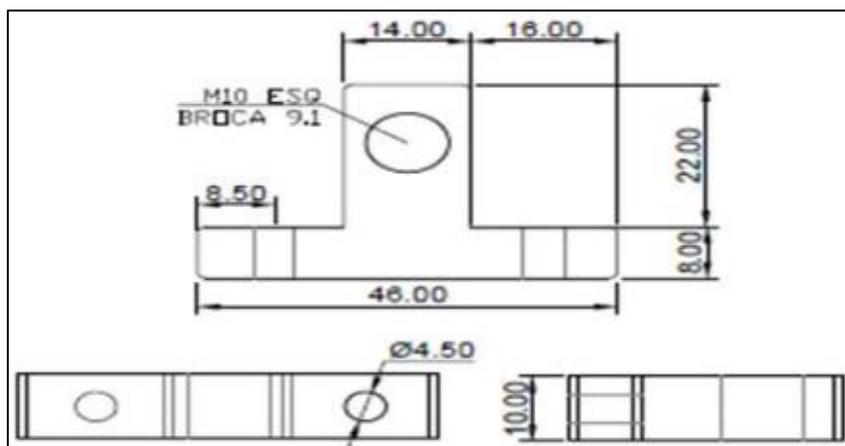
Desenho em CAD do suporte de cilindro pneumático.
